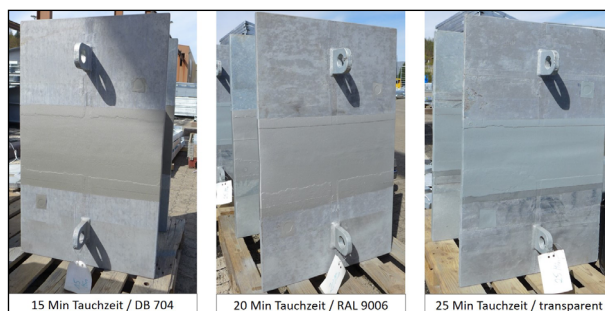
Fertiggestellte Arbeitsproben der Montageschweißstöße mit thermisch gespritztem und versiegeltem Überzug im Bereich der Schweißnaht (IKS)
